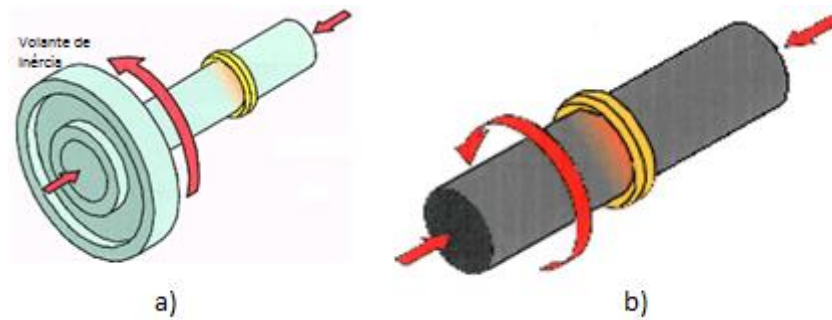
Soldadura por fricção rotacional: a) inércia; b) contínua
